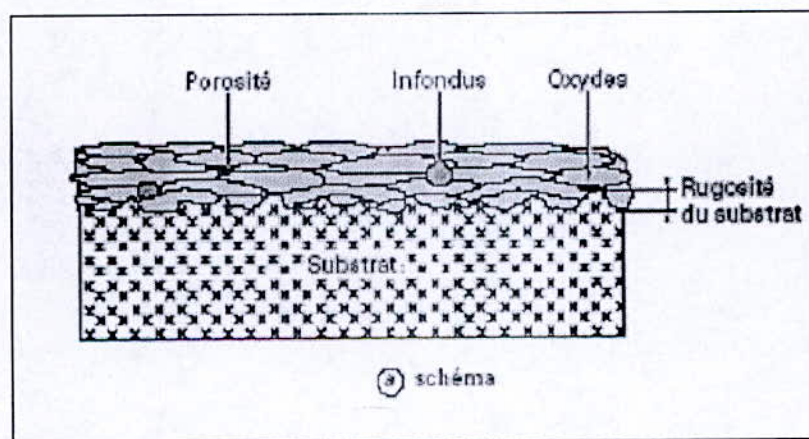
coupe d'un dépôt obtenu par rechargement par soudage [6]
